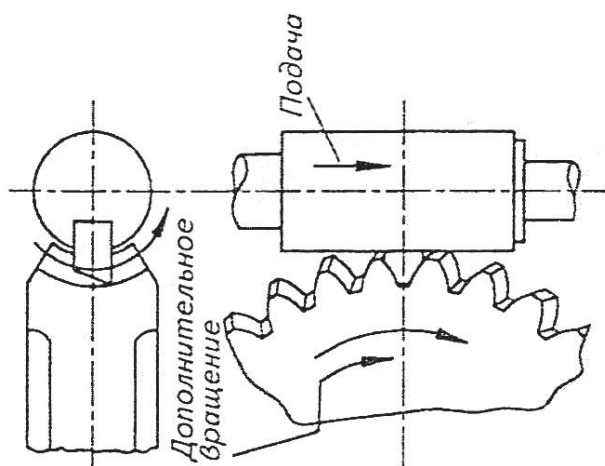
Схема нарезания зубьев червячного колеса «летучим» резцом
